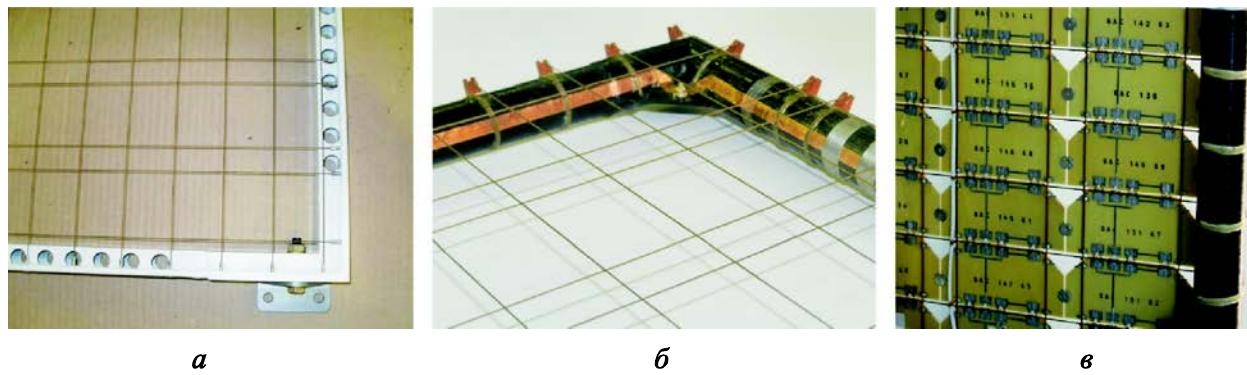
Фрагменты конструкций трубчатых каркасов СБ:
